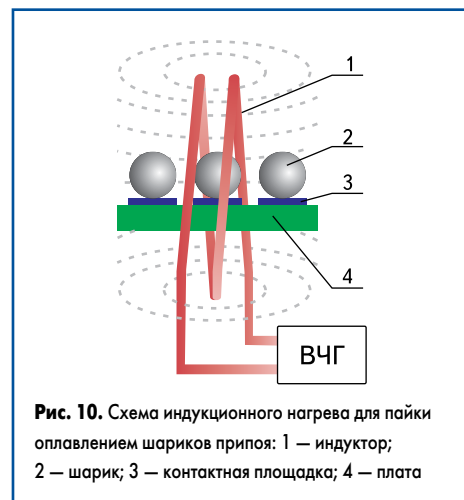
Схема индукционного нагрева для пайки оплавлением шариков припоя: 1 — индуктор; 2 — шарик; 3 — контактная площадка; 4 — плата
